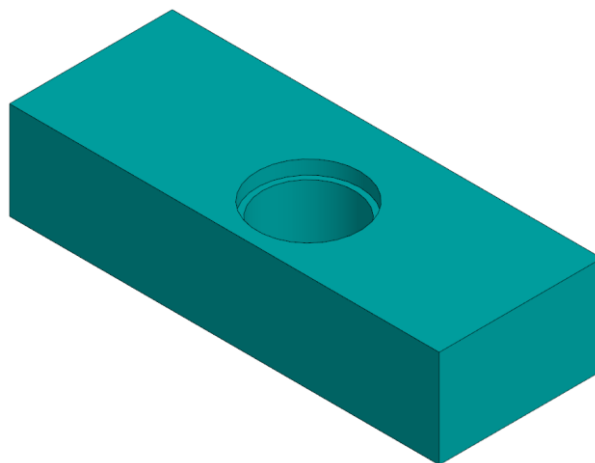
Заготовка поворотного кулака перед установкой на стол фрезерного станка
